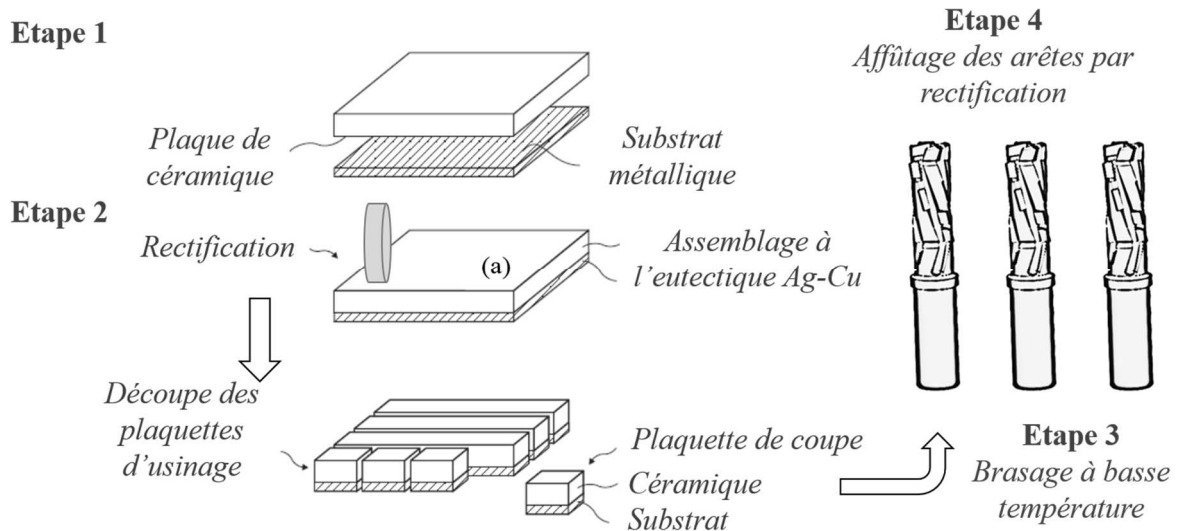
Etapes de fabrication d'outils prototypes pour l'usinage
